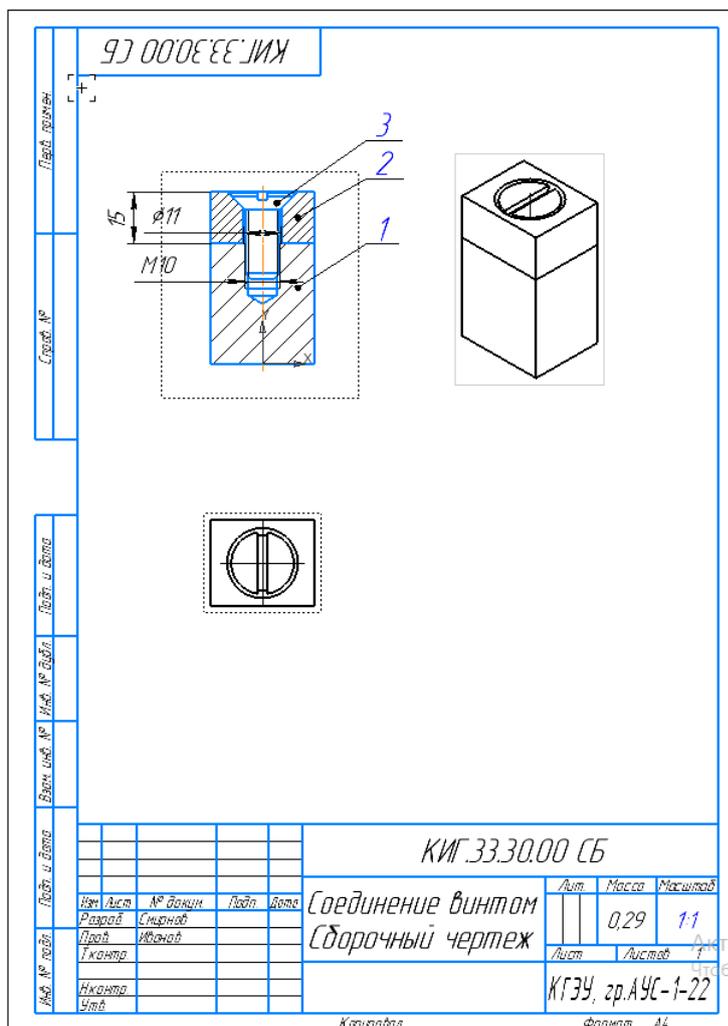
Сборочный чертеж соединения винтом с потайной головкой
